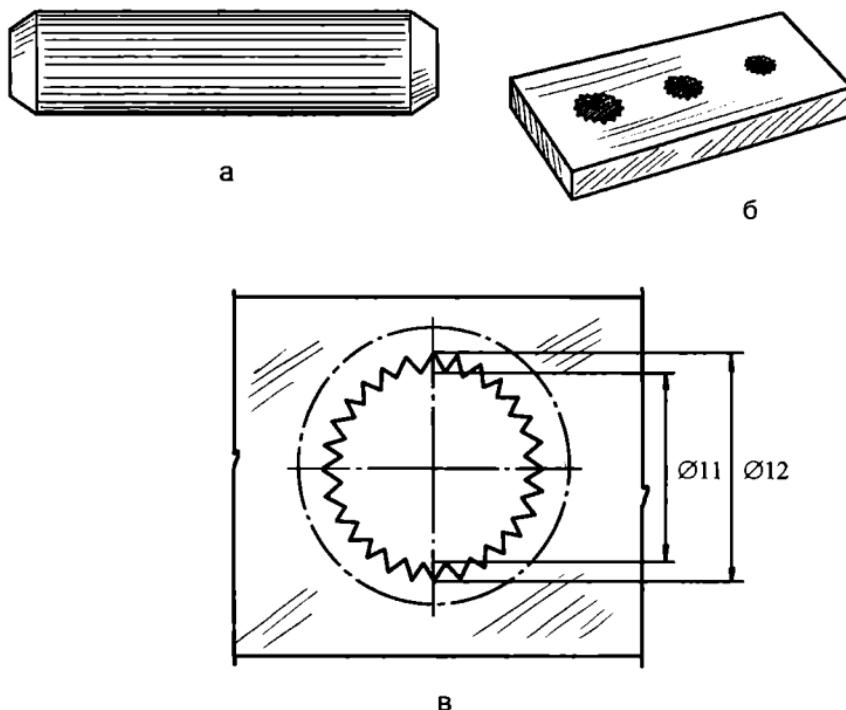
Конструкция шканта: а — шкант; б — калибр; в — схема изготовления калибра
